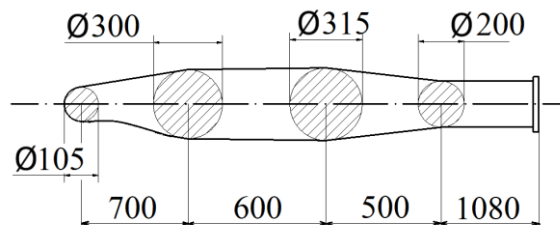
Ескіз прямої стрижневої заготовки гака перед операцією згинання
